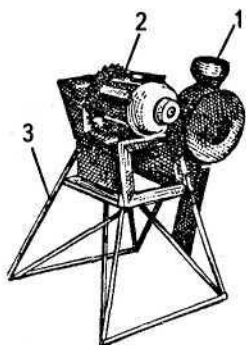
Мельница-зернодробилка. *Первый вариант устройства:
